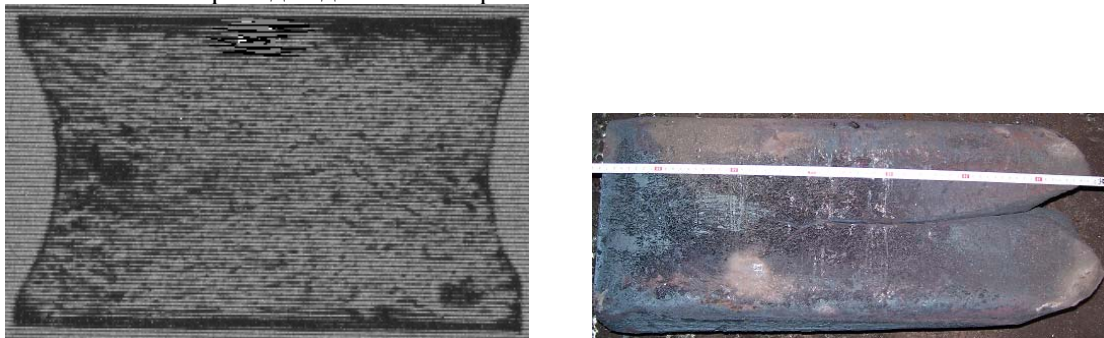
Форма боковой и торцевой поверхности раската: а – после прокатки первых проходах; б – в конце прокатки
